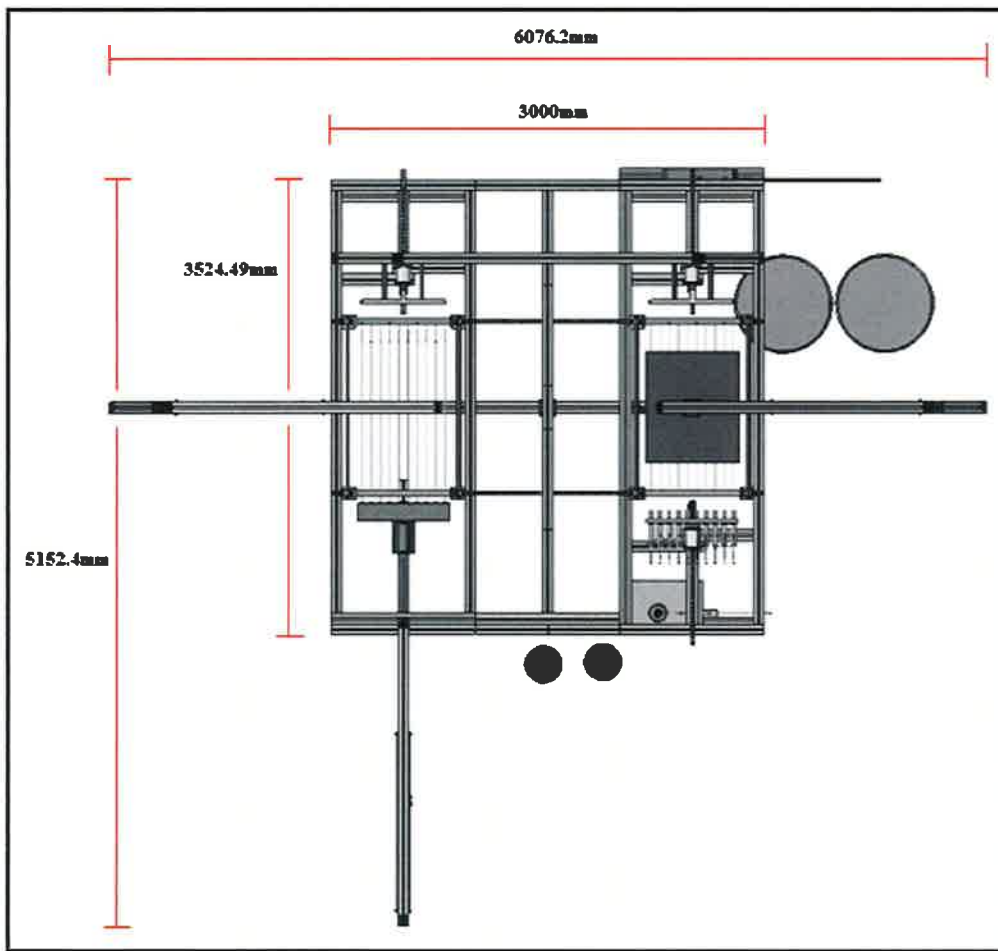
Dimensiones de máquina NTC terminada, vista superior.
